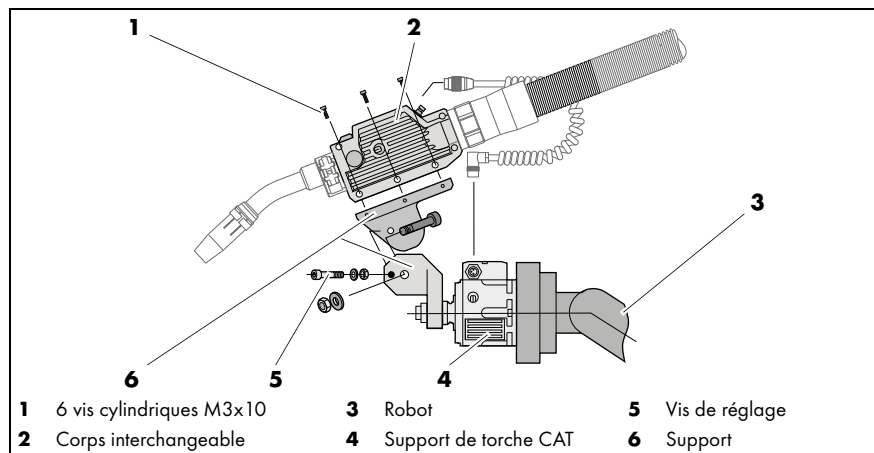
Monter le système de torche de soudage sur le robot
